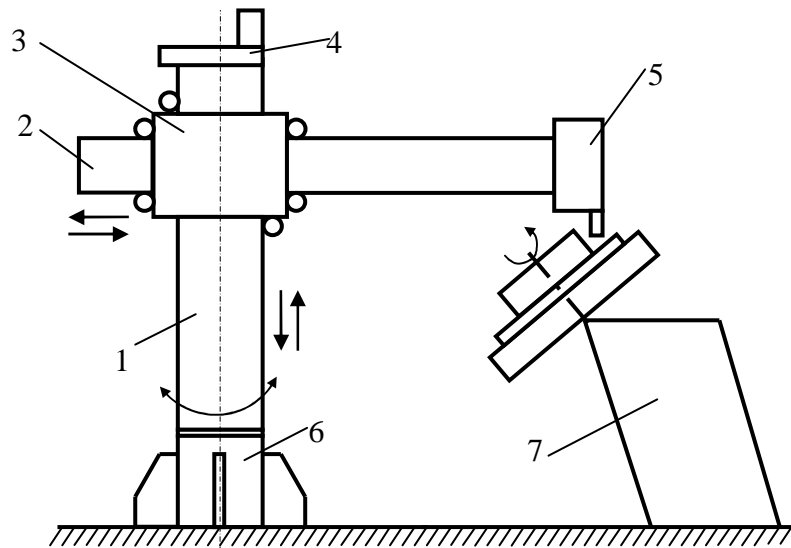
Колонна підйомно-поворотна для несамохідних зварювальних апаратів: 1 – стояк поворотний; 2 – консоль висувна; 3 – каретка; 4 – привод піднімання і опускання; 5 – несамохідний зварювальний апарат; 6 – основа колони; 7 – маніпулятор.
